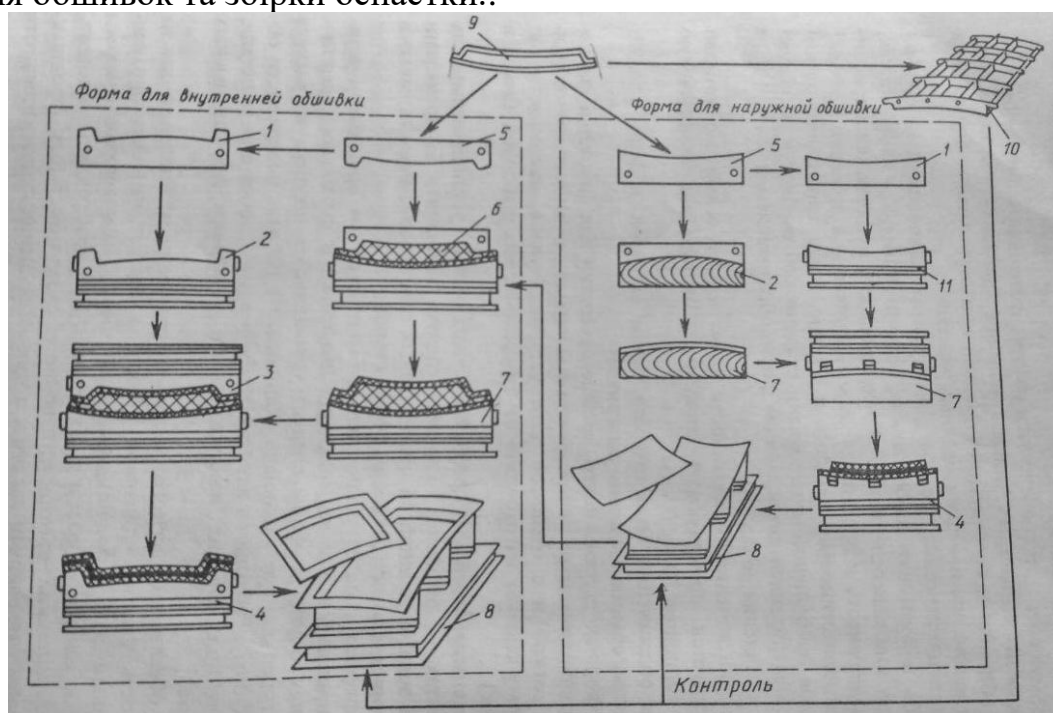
Схема ув'язки і виготовлення оснастки для формування обшивок з КМ
